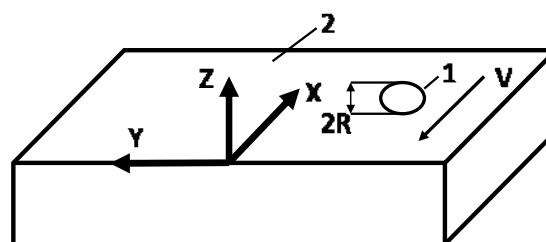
Схема расположения лазерного пучка в зоне обработки
